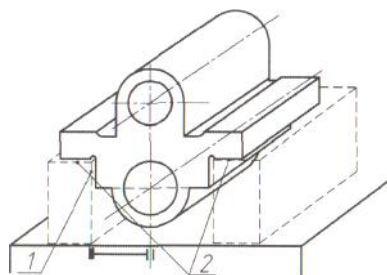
Схема установки заготовки с разделенными базовыми опорными поверхностями: 1 – базовая боковая опорная поверхность; 2 – базовые установочные опорные поверхности
